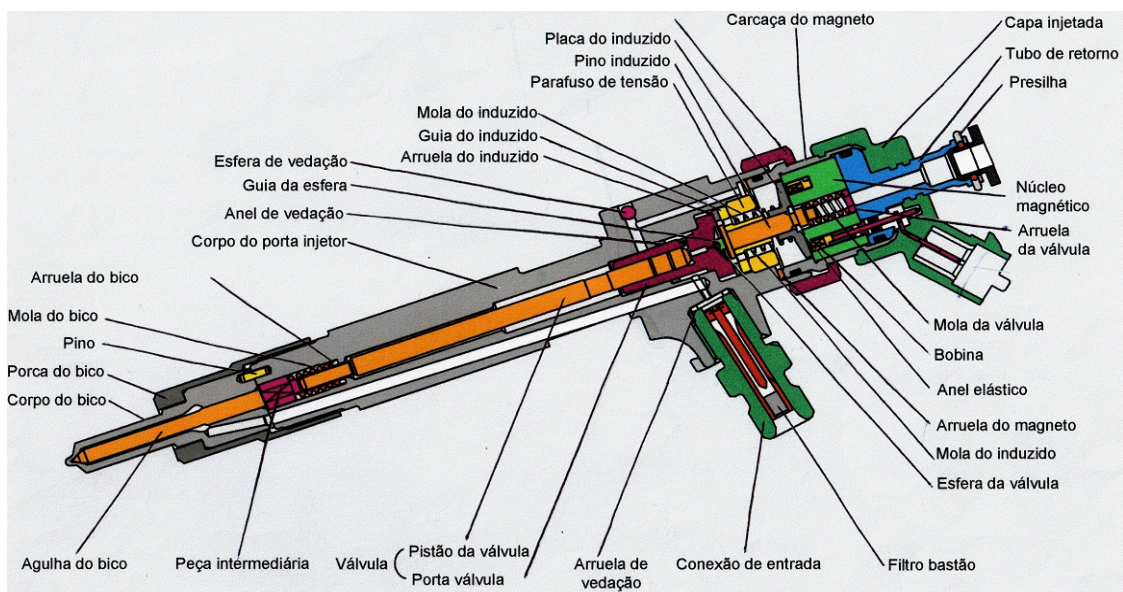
Injetor *Common Rail Bosch* em pormenor, adaptado de [51].
